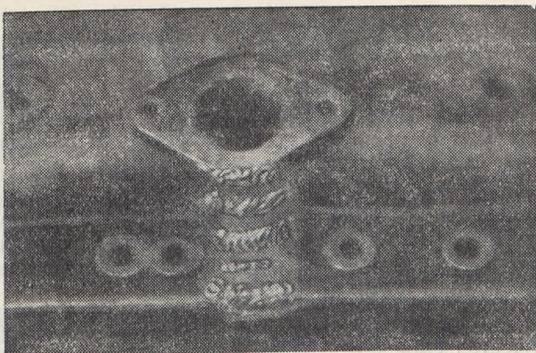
Примеры заварки трещин в головках блоков цилиндров двигателя ЗИС-5 наложением поперечных швов.
